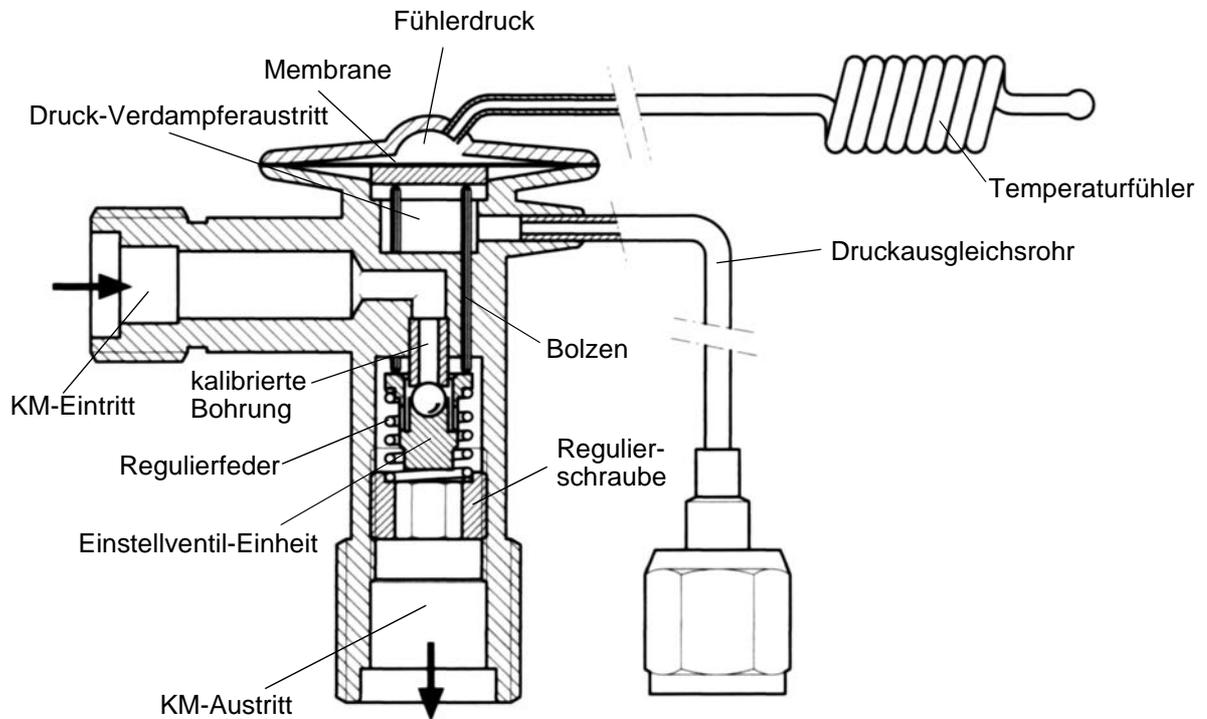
TEV mit äußerem Druckausgleich (Eckventil)
